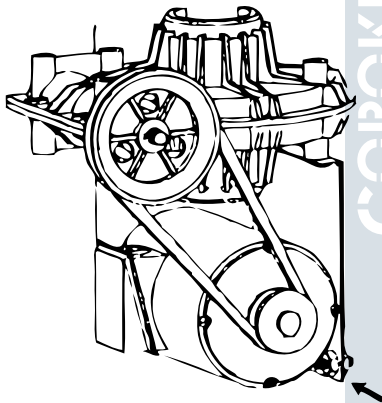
Натяжение клинового ремня электродвижения стола
